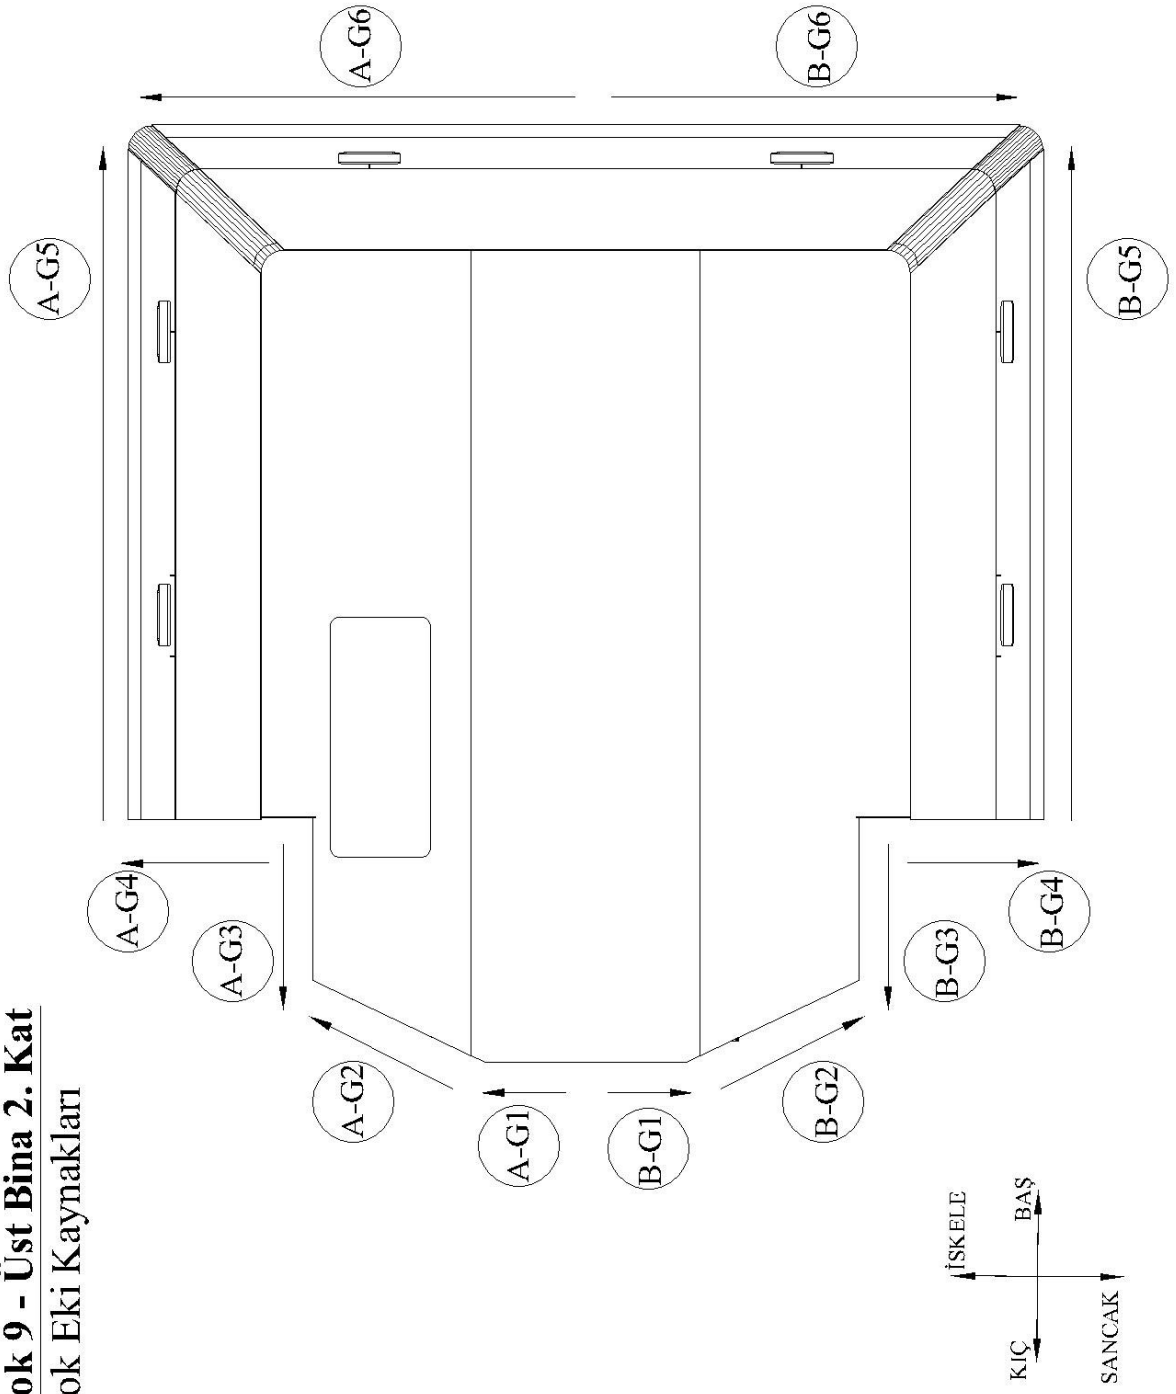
Blok 9 Üst bina 2.kat tüm panellerin montajı
